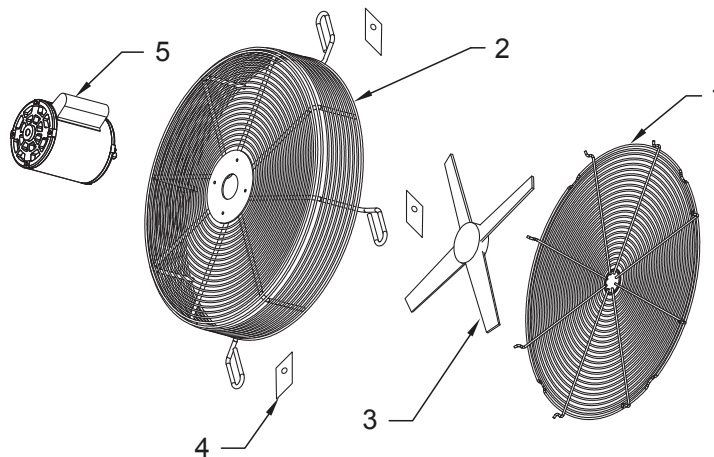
Pièces de rechange pour ventilateur Guard-Mount
